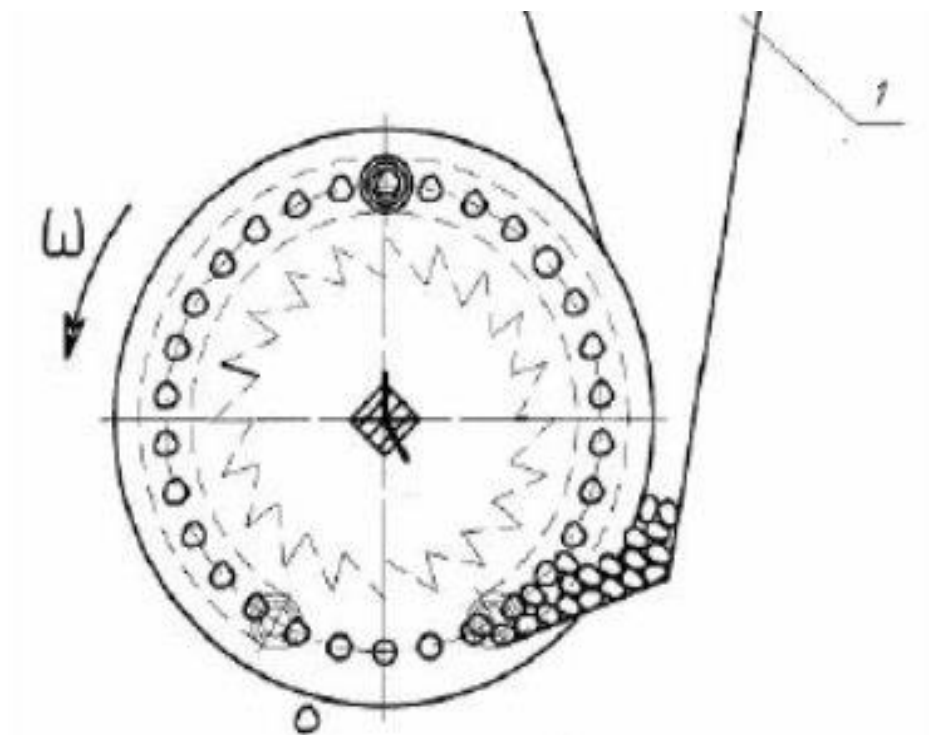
Пневматичний висівний апарат (Український корисний зразок № 3625)
